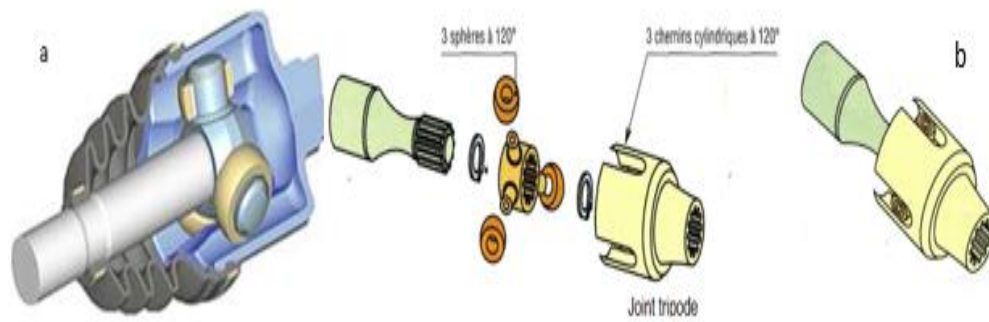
a) Joint tripode, b) vue éclatée.
